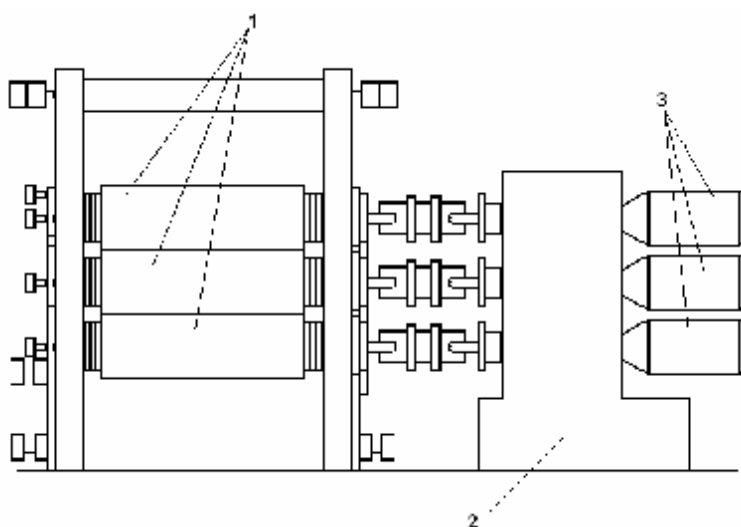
Схема трехвалкового каландра: 1 – валки; 2 – приводной блок; 3 – двигатели.
